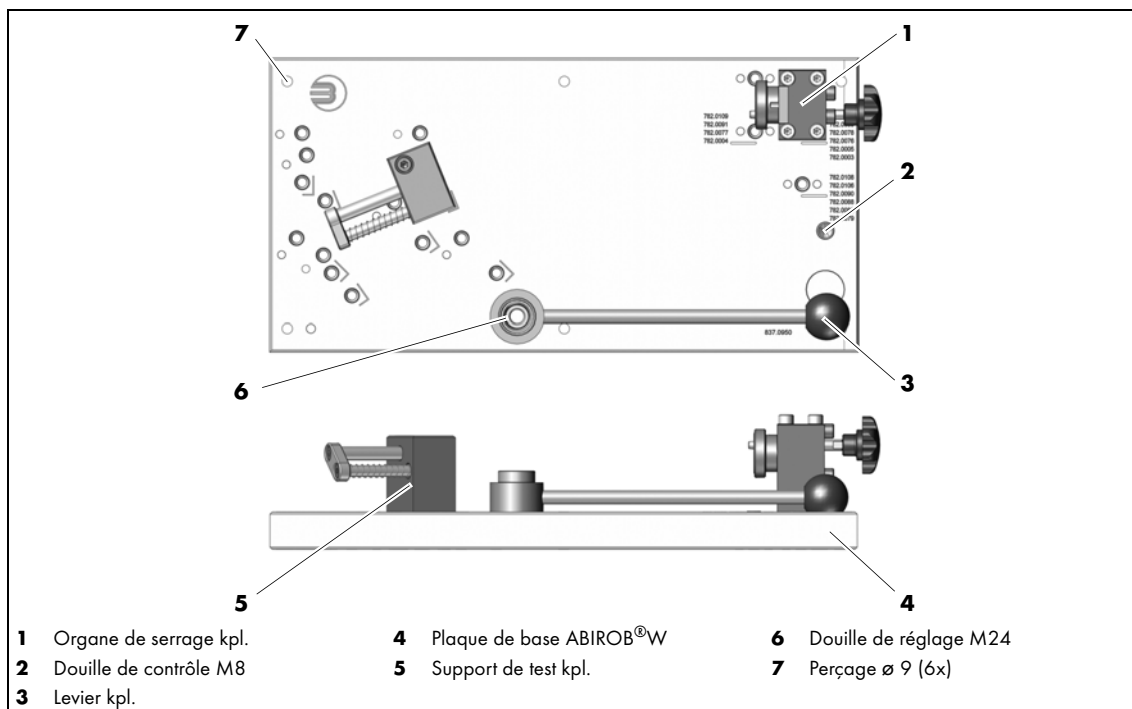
Installer le marbre de contrôle et de rectification ABIROB®W
